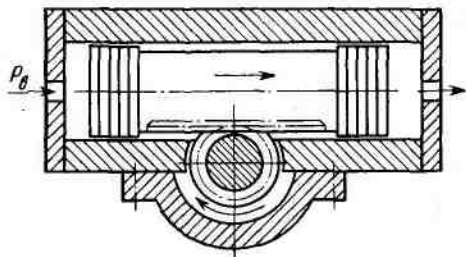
Поворотный пневмоцилиндр (p_a — давление воздуха)
